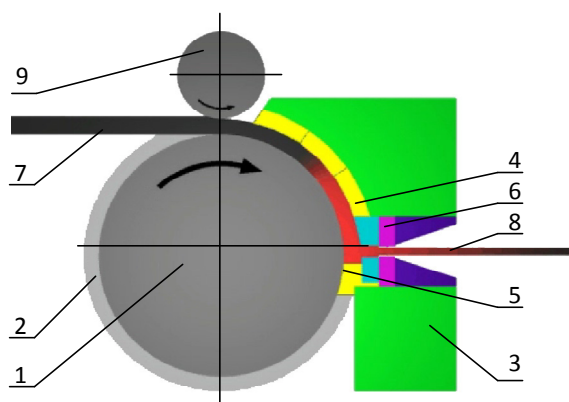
Принципиальная схема реализации процесса непрерывного прессования по способу Конформ: 1 – рабочее колесо, 2 – кольцевая канавка, 3 – башмак, 4 – кольцевая вставка, 5 – вставка, 6 – матрица, 7 – заготовка, 8 – изделие, 9 – валок
